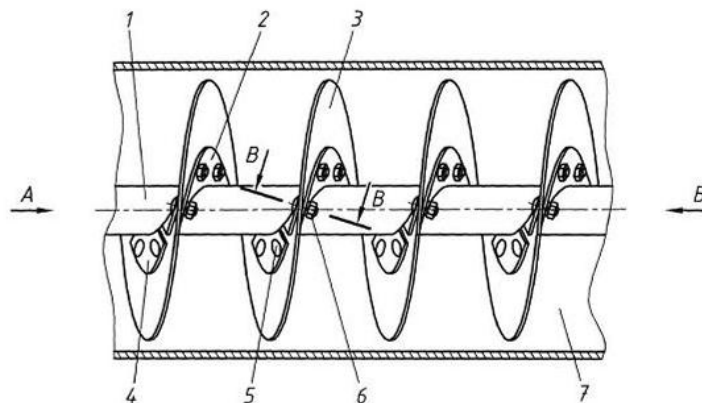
Загальний вигляд модернізованого шнека з суцільною еластичною гвинтовою поверхнею: 1 – центральний вал; 2 – несуча смугова гвинтова спіраль; 3 – робоча еластична спіраль; 4 – секційна гвинтова пластина; 5 – болтове з'єднання з напівкруглою головкою; 6 – гайка з гравером; 7 – кожух дозатора
